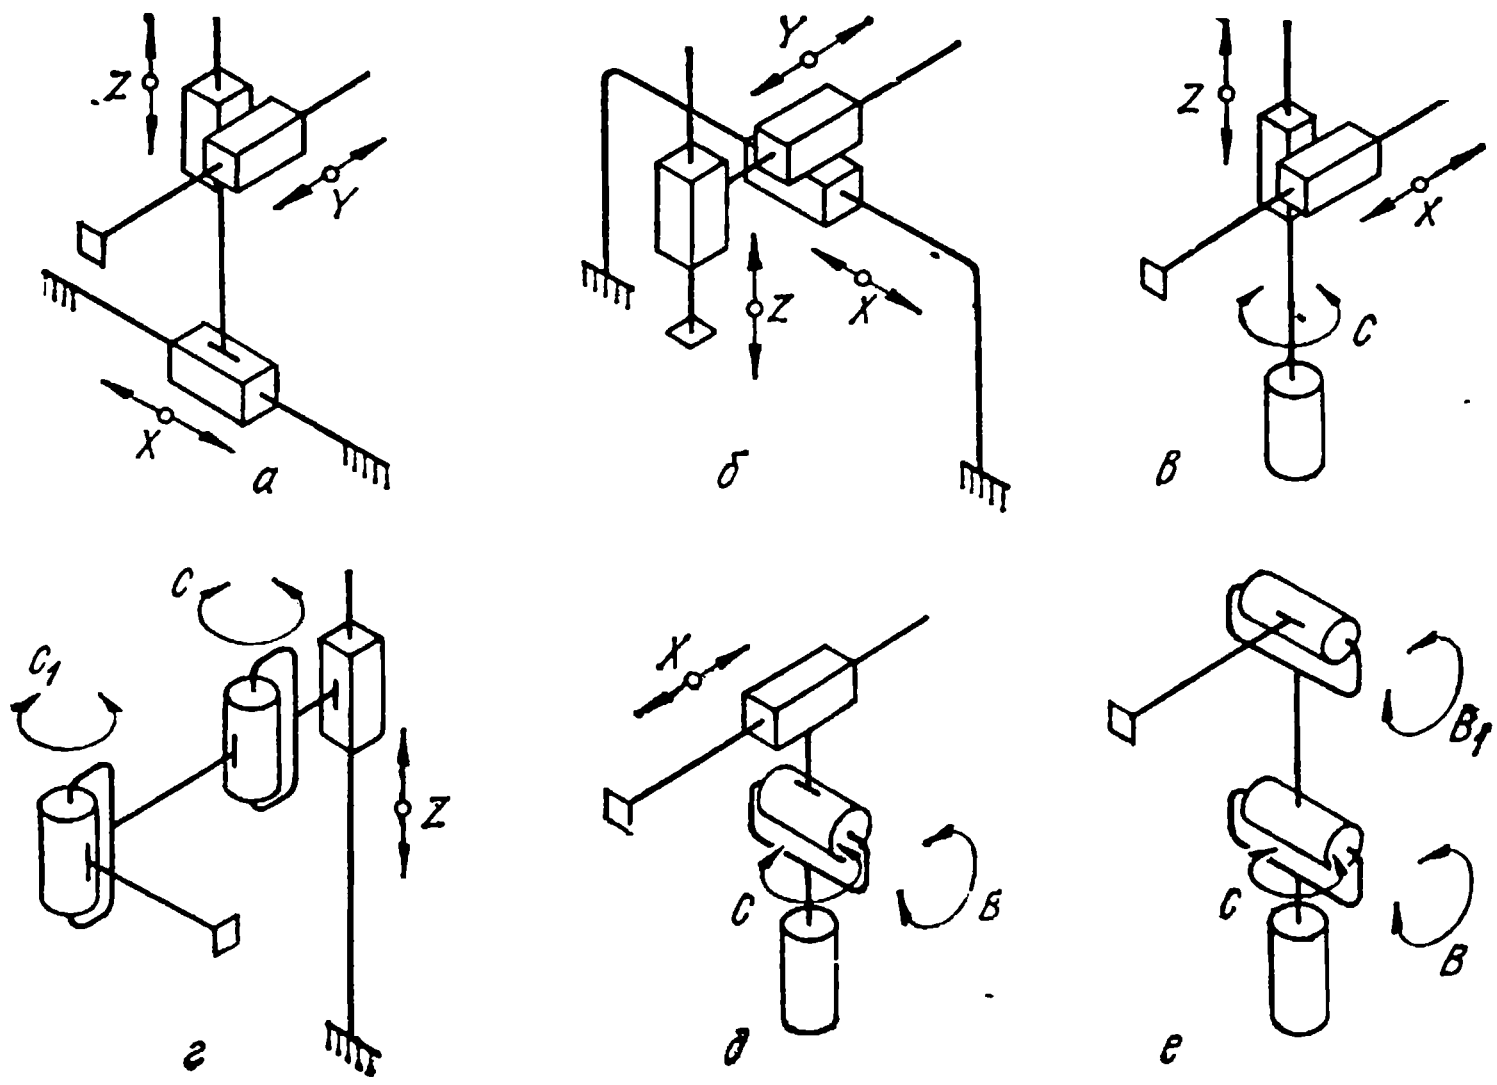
Структурные схемы основных типов манипуляторов сварочного инструмента с прямоугольной (а, б), цилиндрической (в), двухполярной цилиндрической (г), сферической (д) и двухполярной сферической (антропоморфной) (е) системами координат переносных движений
